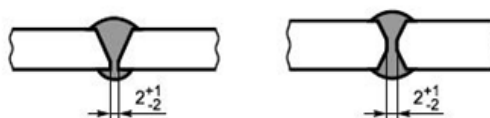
Виды вертикальных сварных соединений стенки.
